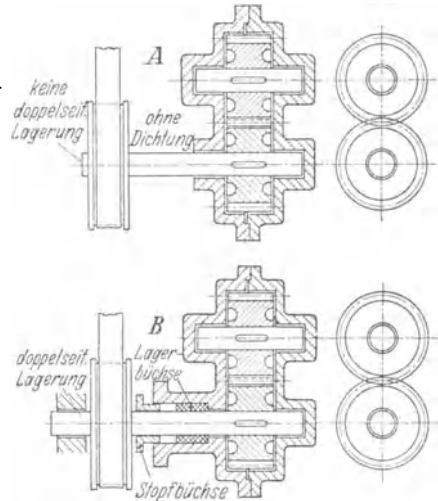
Pumpe mit schlechter und guter Abdichtung.
